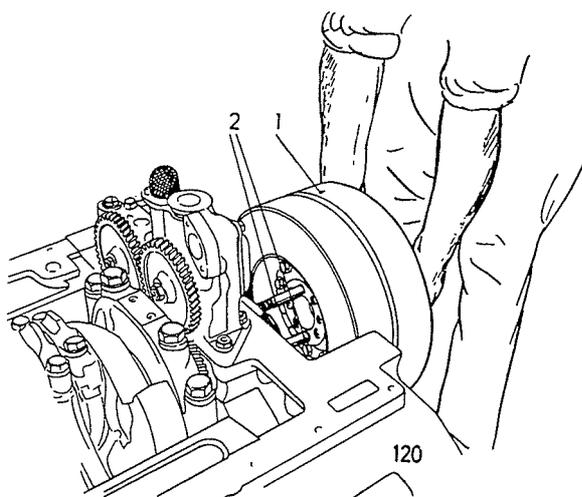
Montage des Schwingungsdämpfers F/A 12L 614
